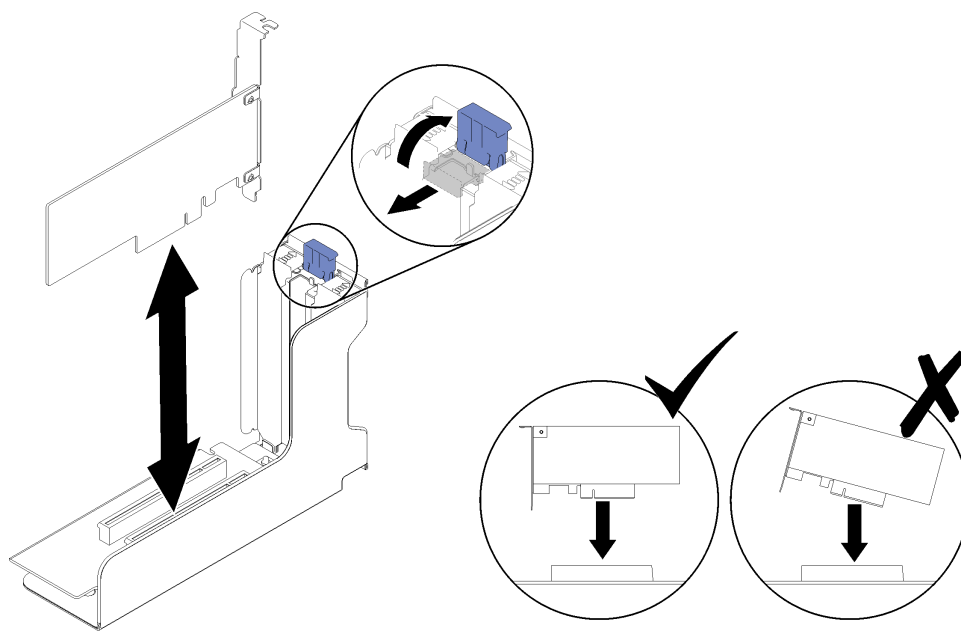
Instalação do adaptador na Conjunto da placa riser PCIe
